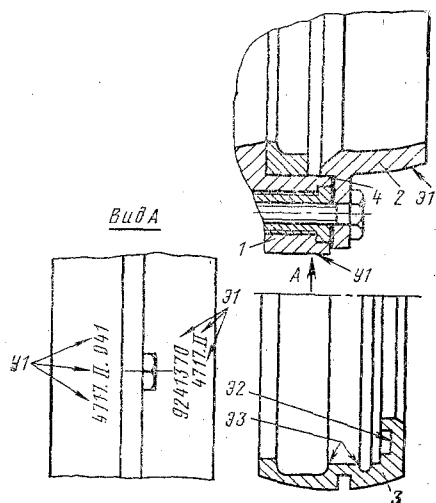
Места маркировки деталей на сферическом соединении двига- теля с главным редуктором:
